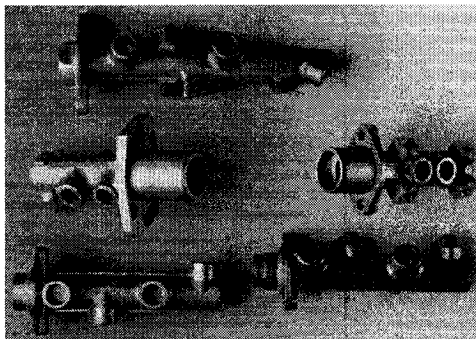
Maître-cylindres de freins fabriqués par thixo-forgeage [41]
